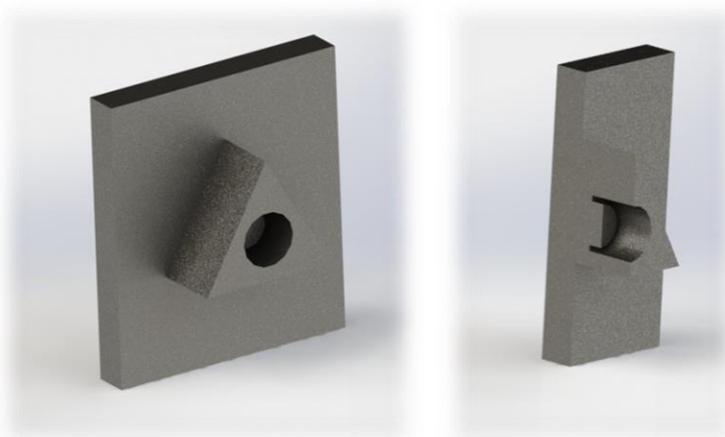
Parte 1 molde cuerpo prisma triangular
